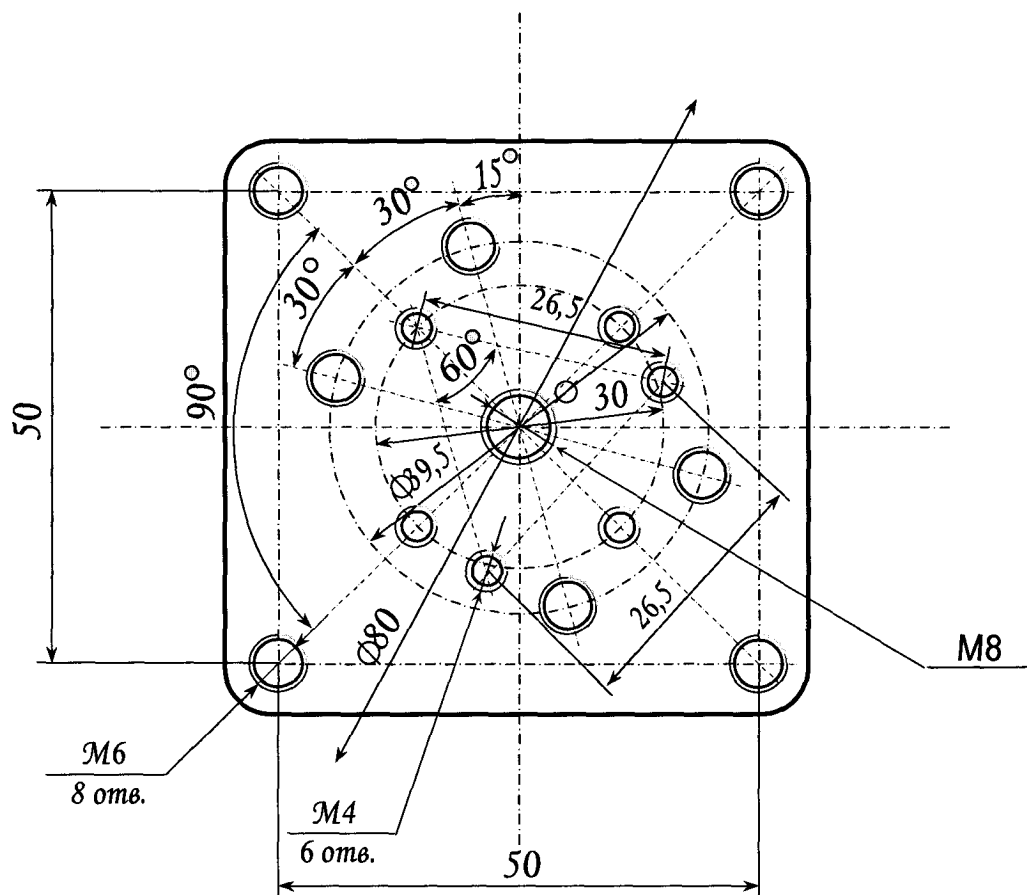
Присоединительные размеры вибростола и расположение резьбовых отверстий для установки поверяемых вибропреобразователей
